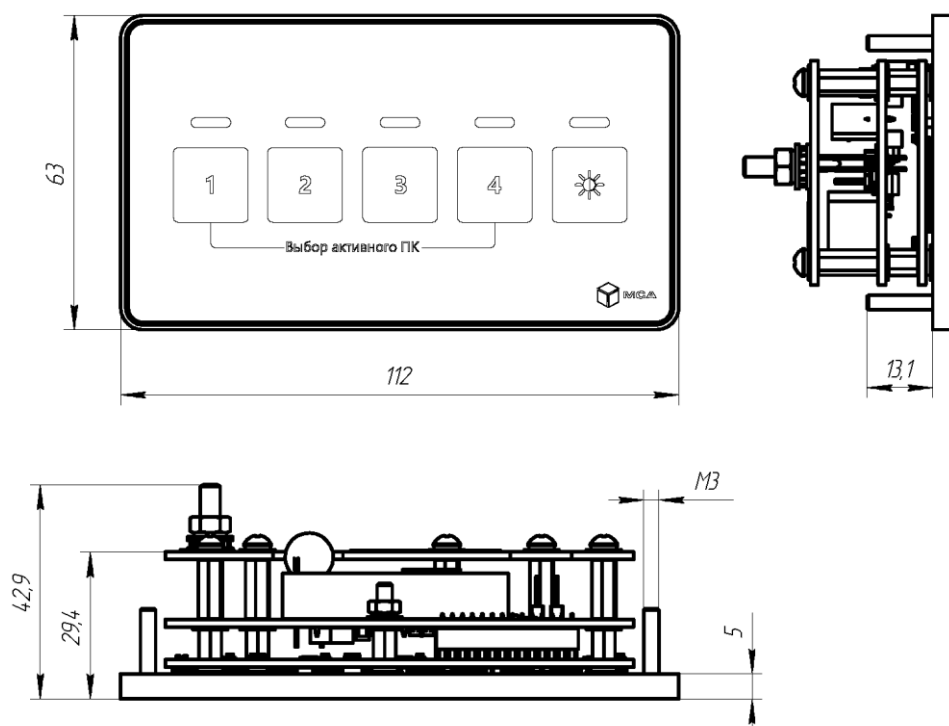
Габаритные размеры КУВВ-143-ПУ104
